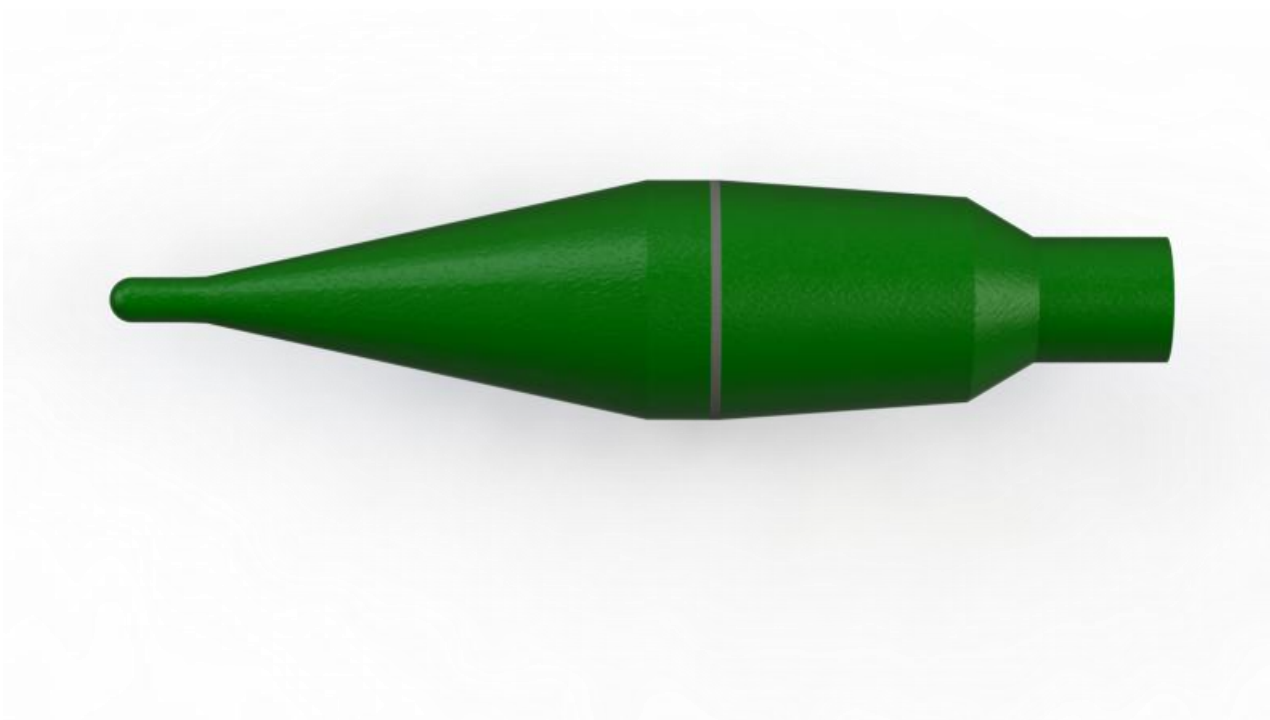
Загальний вигляд корпусу в зібраному стані.
